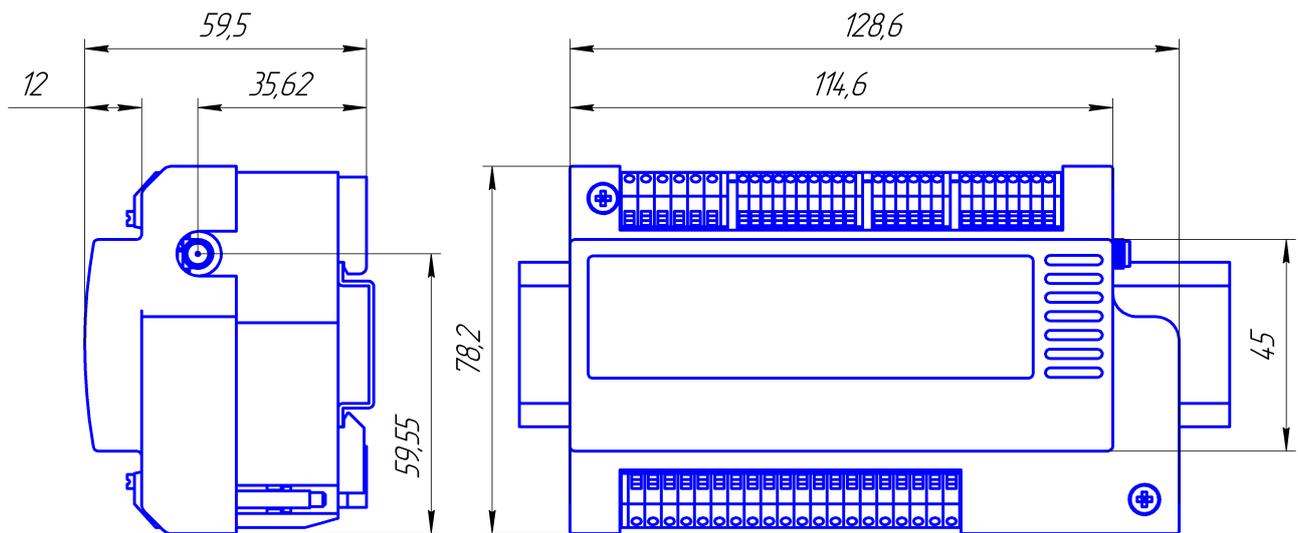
Габаритные и установочные размеры контроллера с креплением на DIN-рейку
